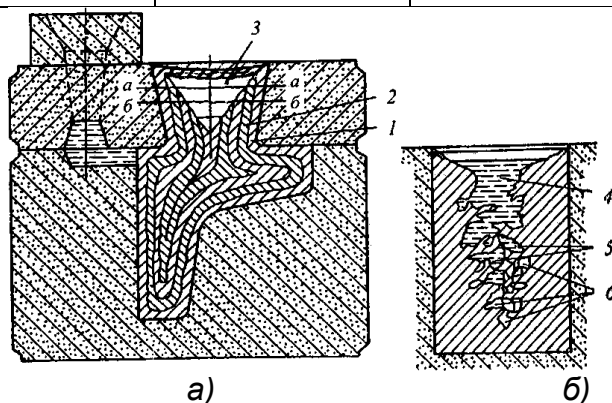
Схема образования усадочной раковины (а) и усадочной пористости (б): 1 – корка твердого металла; 2 – новый твердый слой; 3 – усадочная раковина, 4 – жидкая фаза, 5 – ячейки; 6 – небольшие усадочные раковины
